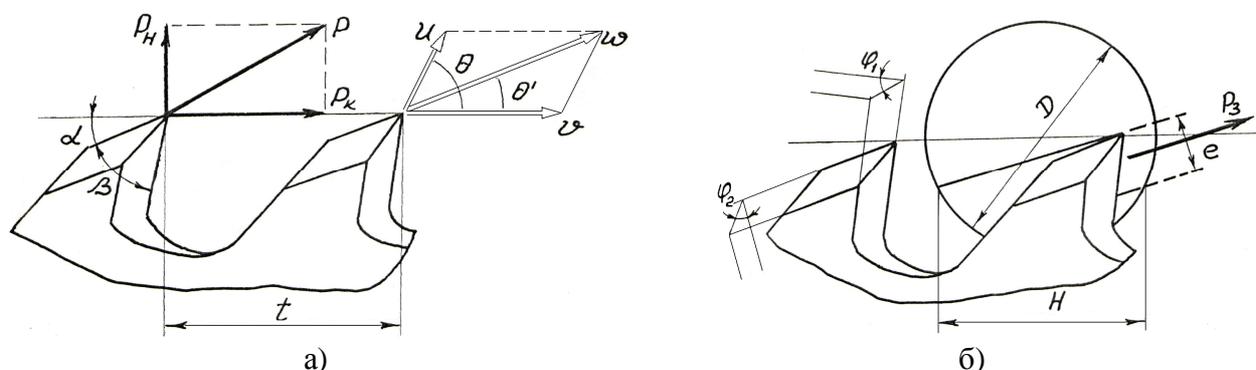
Расчетные схемы для определения усилий бесстружечного резания деревьев зубьями подвижного ножа: D - диаметр среза; t - шаг зубьев; H - высота реза; e - толщина реза; α - контурный задний угол; β - контурный угол заострения; φ_1 - передний угол заострения;
